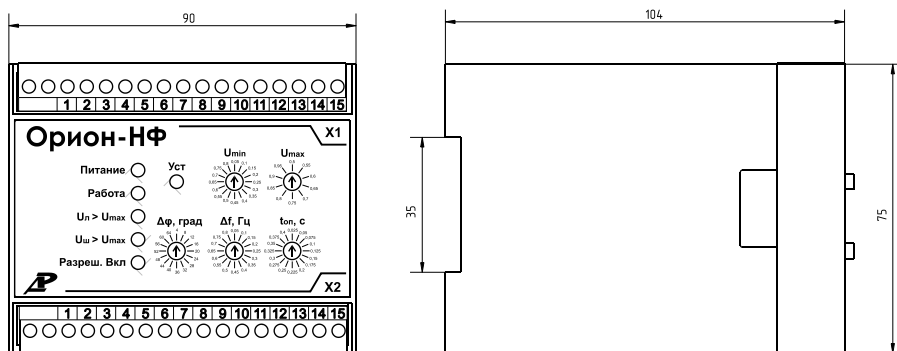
Внешний вид и габаритные размеры устройства «Орион-НФ»
